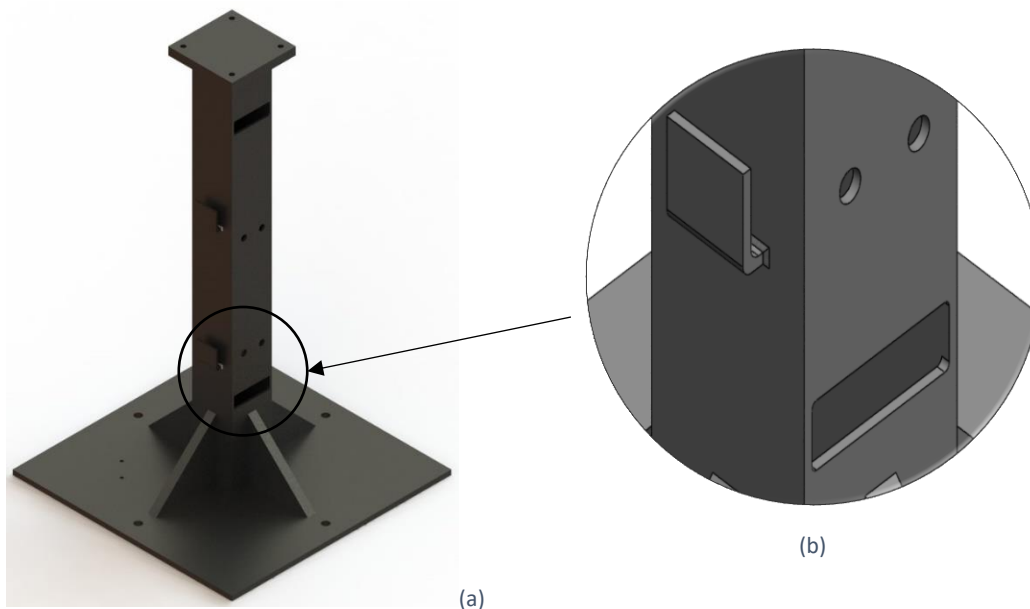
Suporte final do robô: (a) suporte do robô com os furos necessários e aberturas para tubos e fios elétricos e (b) detalhe da soldadura do suporte do controlador do robô colaborativo.
